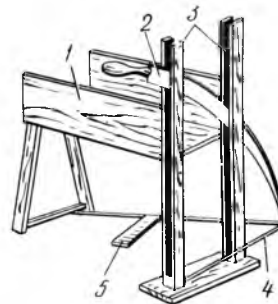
Измельчитель для зеленых кормов: 1 — лоток; 2 — лезвие косы; 3 — паз; 4 — систем рычагов; 5 — педаль
